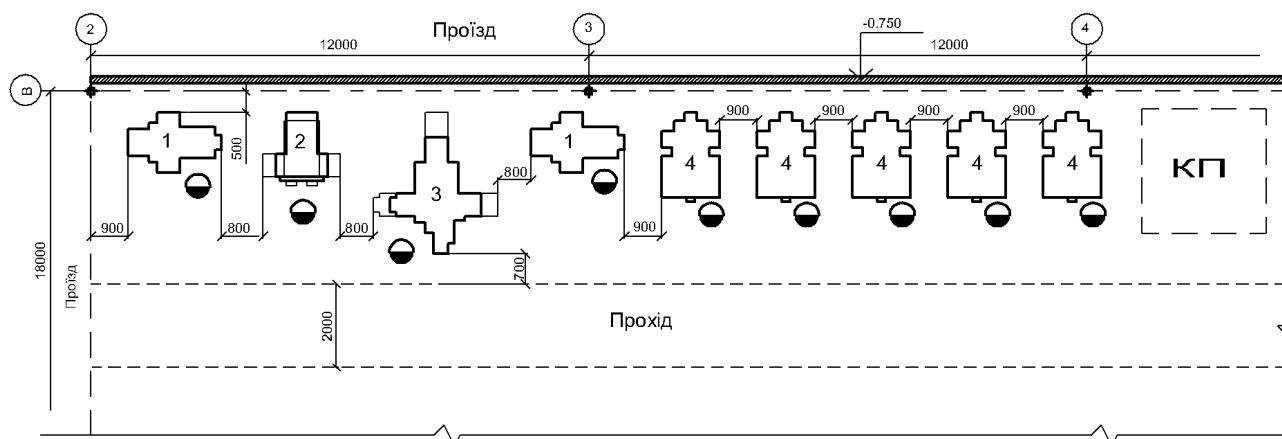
План розміщення обладнання на дільниці механічної обробки корпусу КС6В-48.101:
